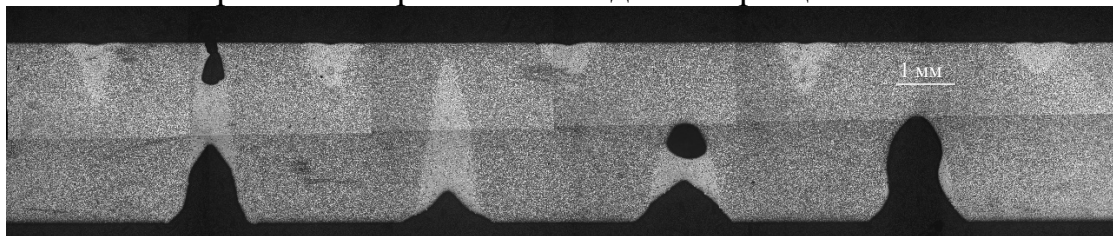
макрошлиф с единичными сварными точками
